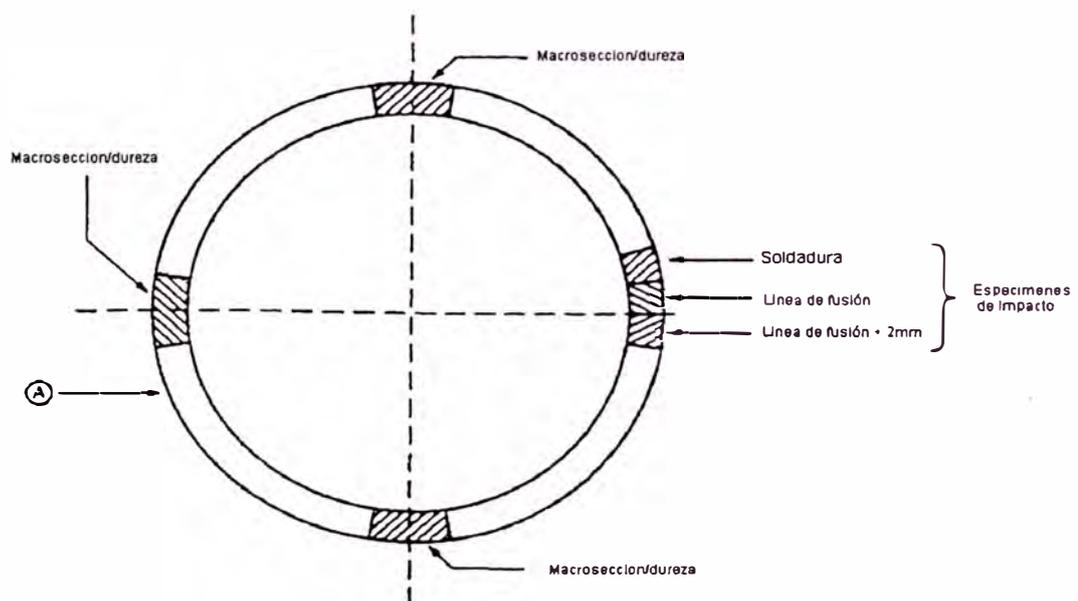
Localización de zonas de control de dureza en soldadura a tope
